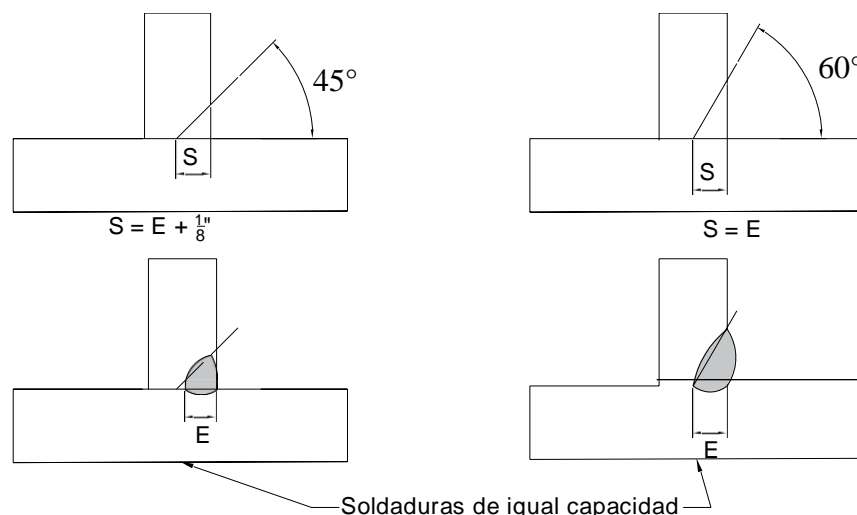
9 Soldaduras de ranura de penetración parcial en la junta, dimensiones "E" y "S".
